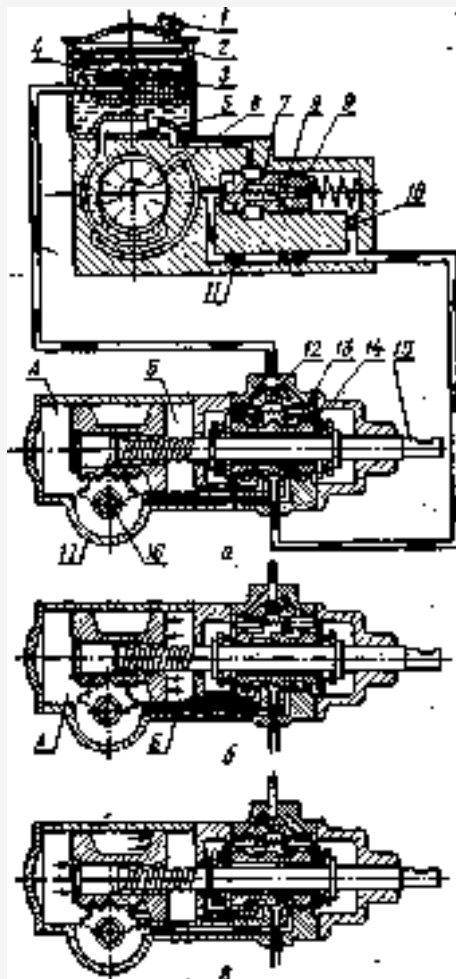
Схема работы гидроусилителя рулевого привода автомобиля ЗИЛ-130
